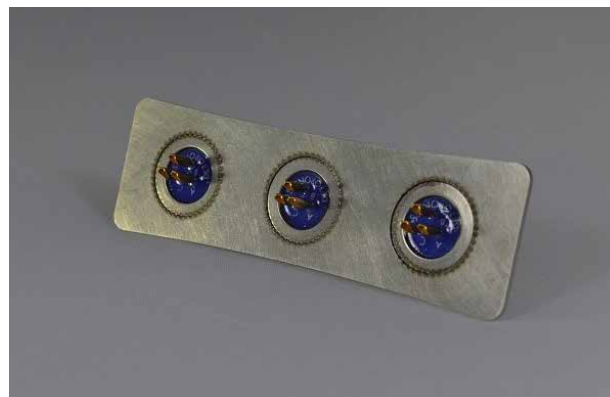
Пример детали, полученной лазерной сваркой тонколистового металла
